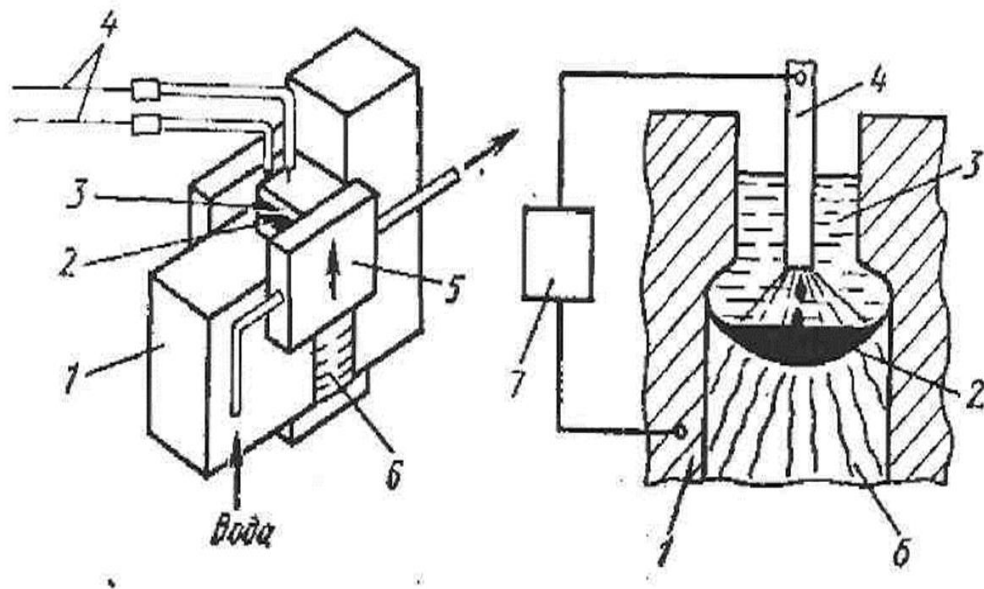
Схема электрошлаковой сварки: 1 - заготовка; 2 - металлическая ванна; 3 - шлаковая ванна; 4 -электродная проволока; 5 - водоохлаждаемый ползун; 6 - сварной шов; 7 - источник питания
